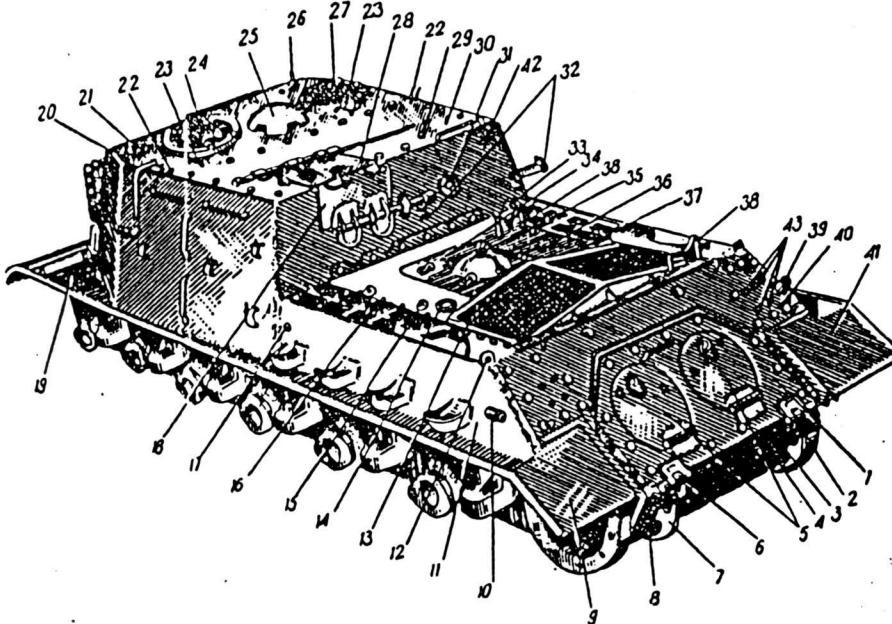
Общий вид корпуса (кормовая часть и крыша):
